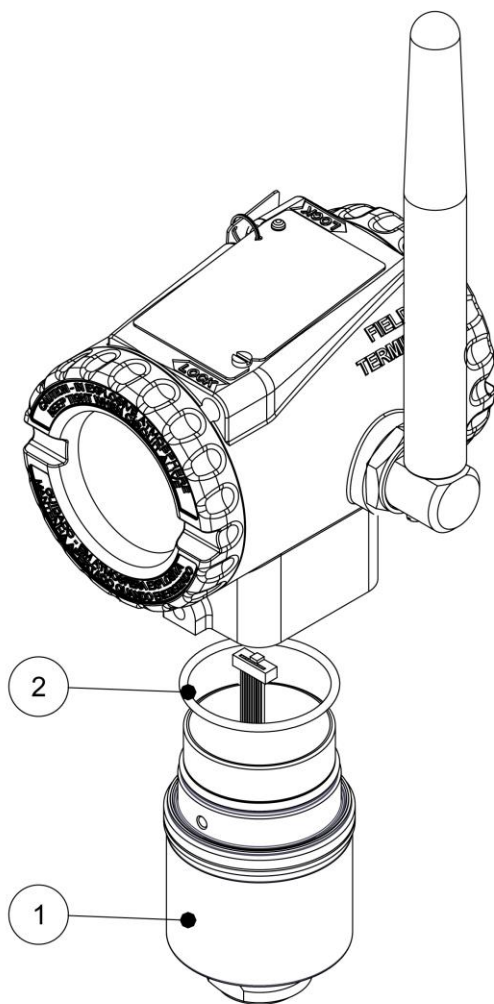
(a) – Vista Explodida – Transmissor de Pressão Diferencial
